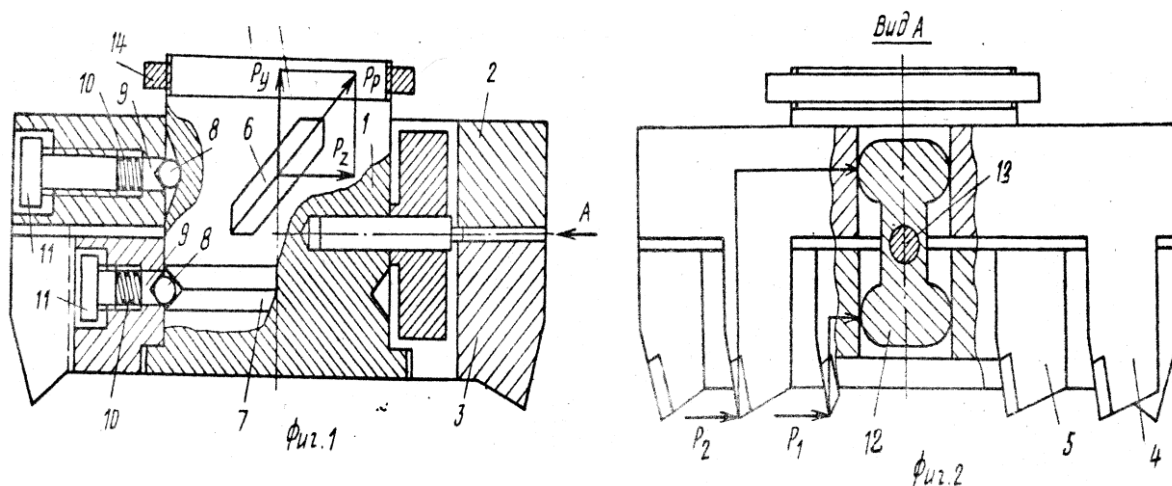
Торцева фреза по а.с. 1053983 МКИ В 23 С 5/06
